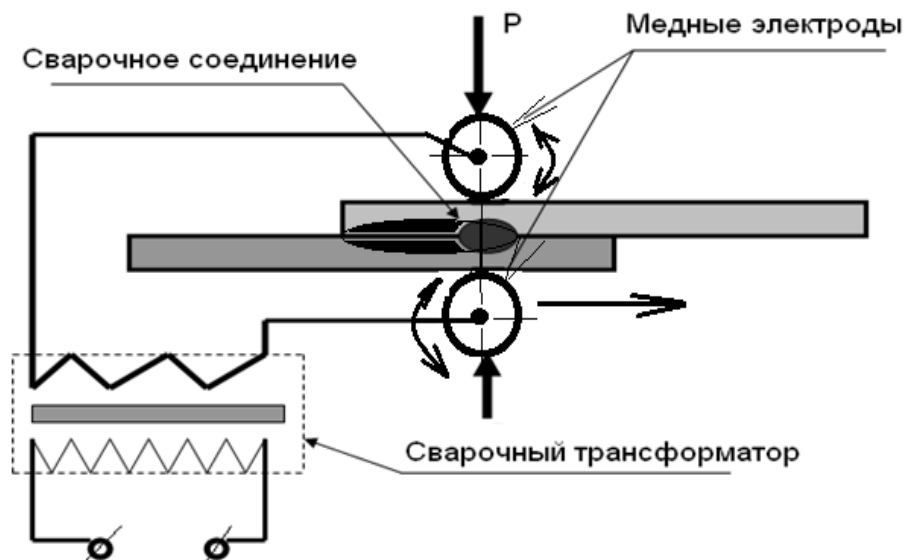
Схема шовной (роликовой) сварки.
